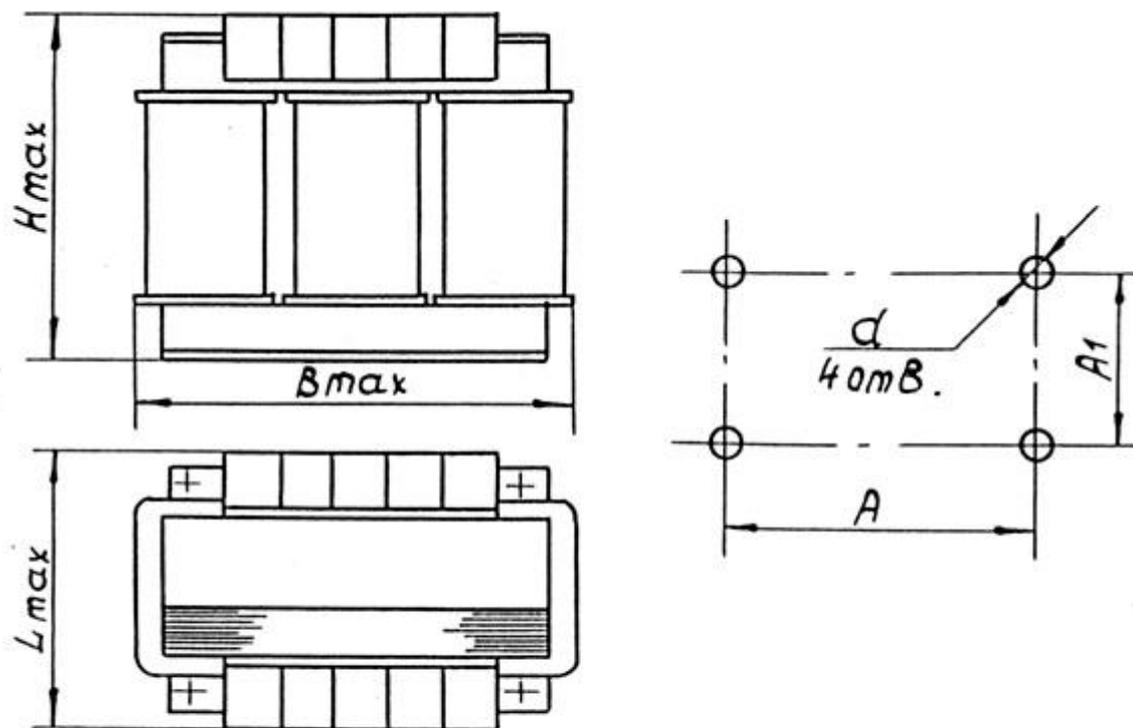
Габаритные размеры, расположение отверстий для установки
